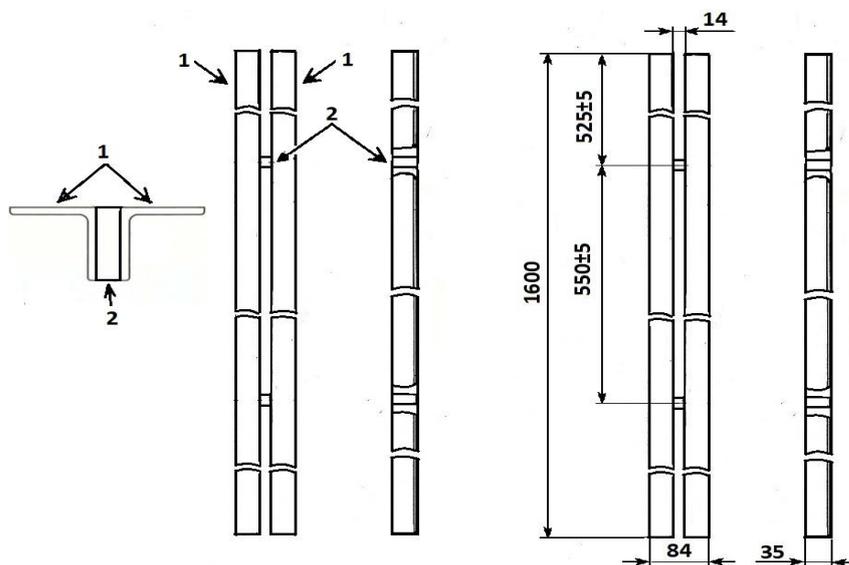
Конструкция и размеры кронштейна типа ККУ-160:
